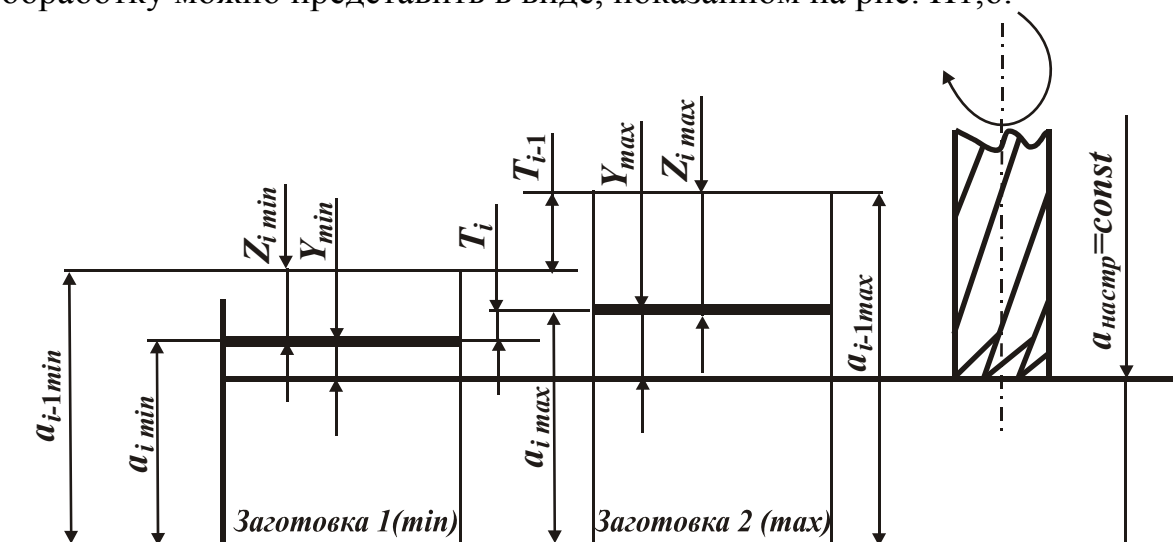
Схема фрезерования двух заготовок на настроенном станке.
